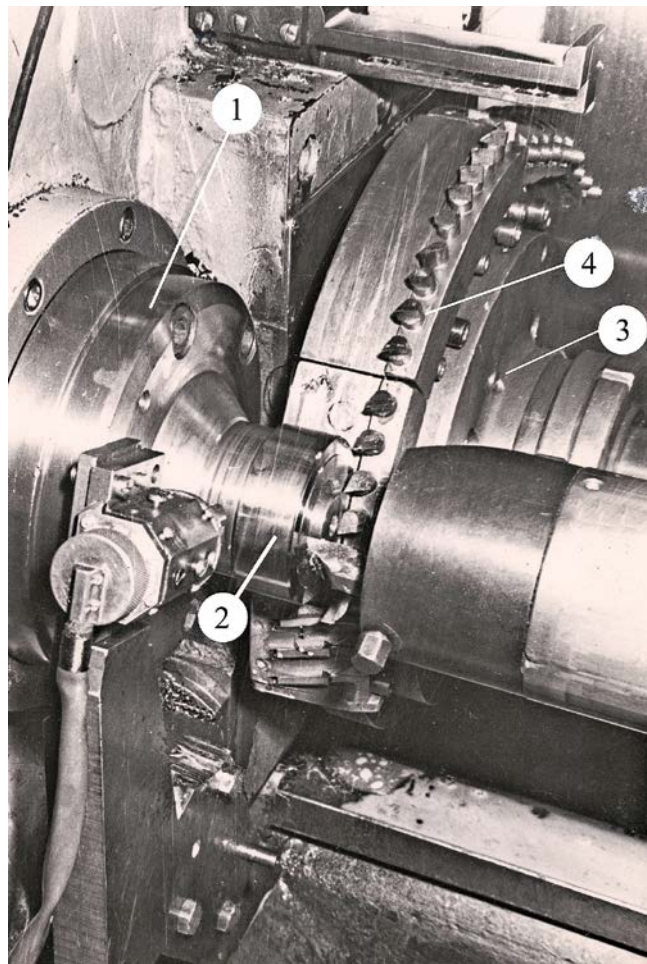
Рабочая зона токарно-протяжного станка. 1 — шпиндель, 2 — заготовка-кольцо, 3 — круглый суппорт, 4 — сегмент протяжки с резцами
